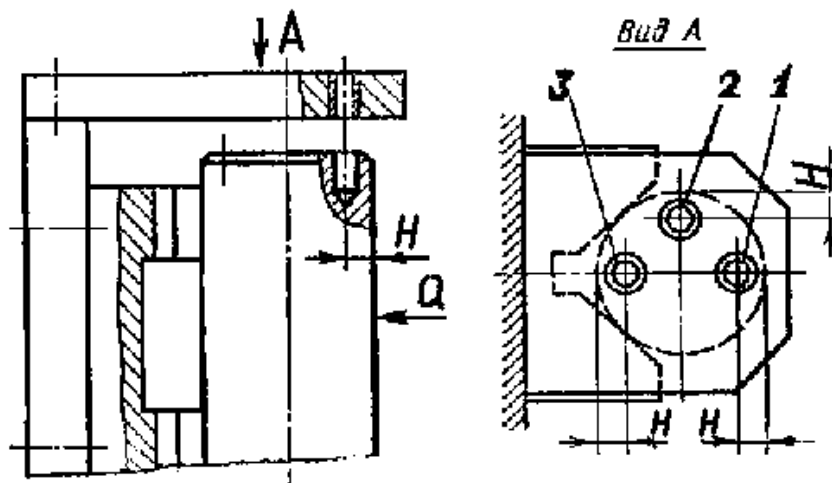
Схема установки кондукторной втулки при сверлении отверстия в торце вала (к задаче 13)
